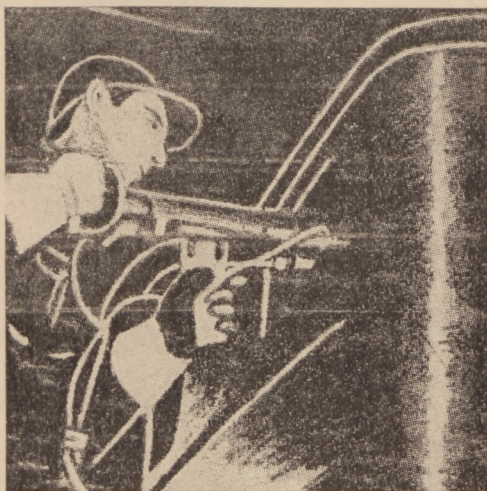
Współczesny aparat punktowy z pneumatycznym napędem górnej elektrody. W wypadku spawania większych połączeń do aparatu może być włączony „pistolet“ do spawania
